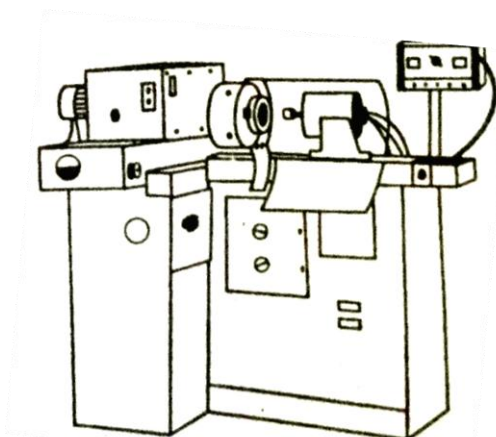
Bezhrotá bruska pro vnější broušení [2].
